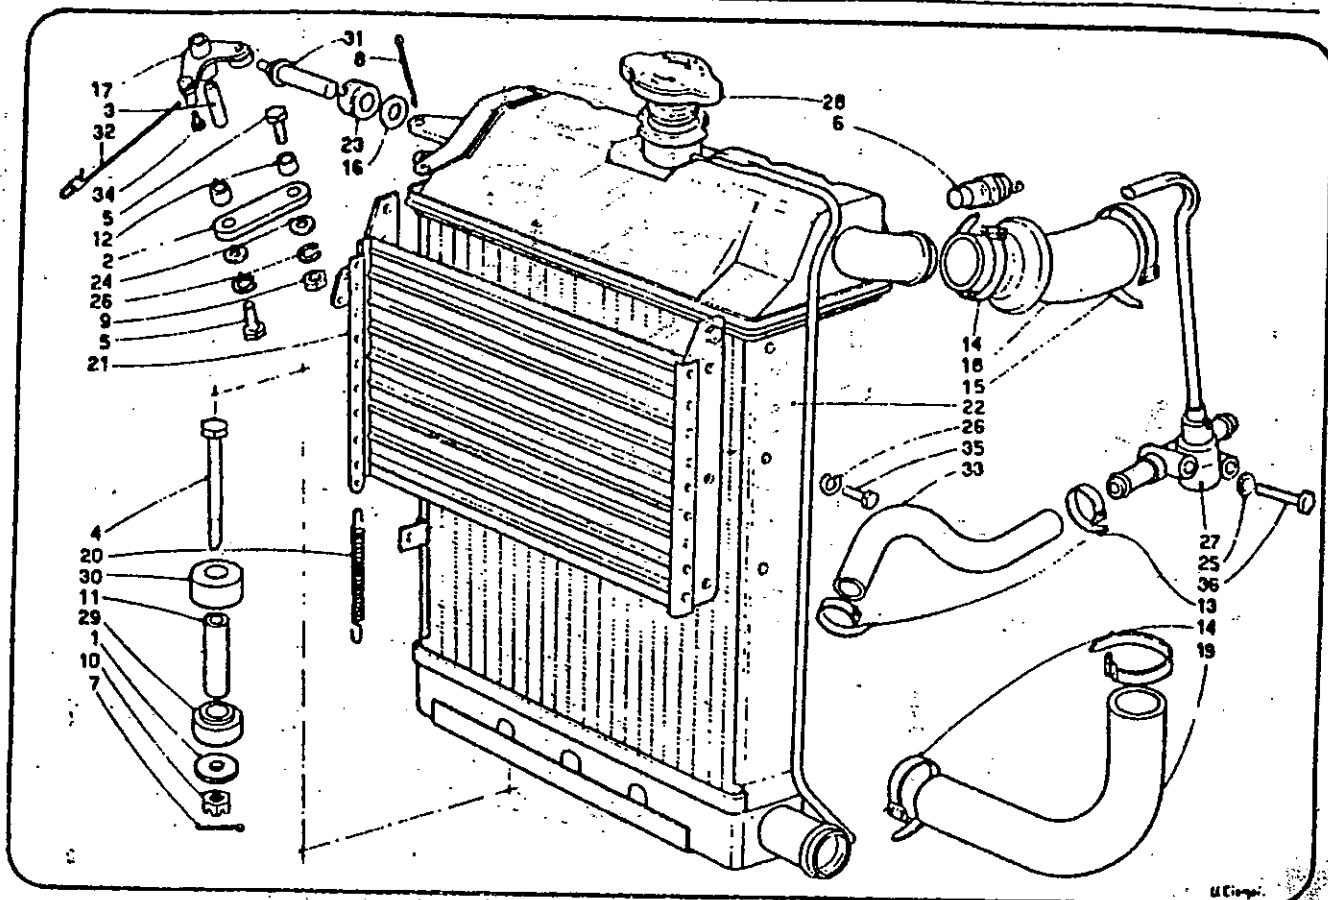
/20 - Radiateur (du Catalogue Pièces Détachées).
